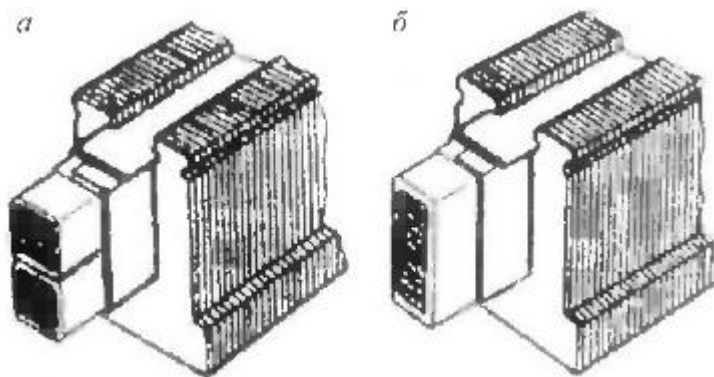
Расположение пазовых сторон двухслойной (а) и однослойной (б) обмоток статора
